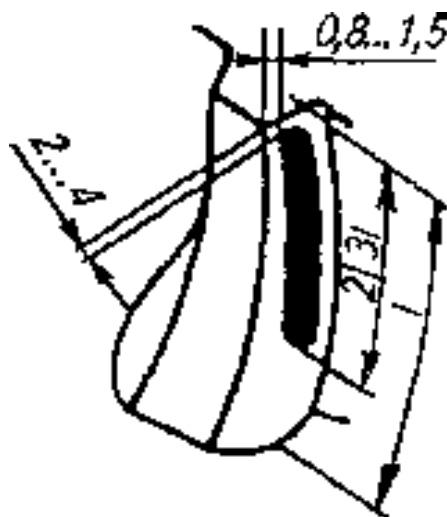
Правильне розташування плями контакту зуба зубчастого колеса:
